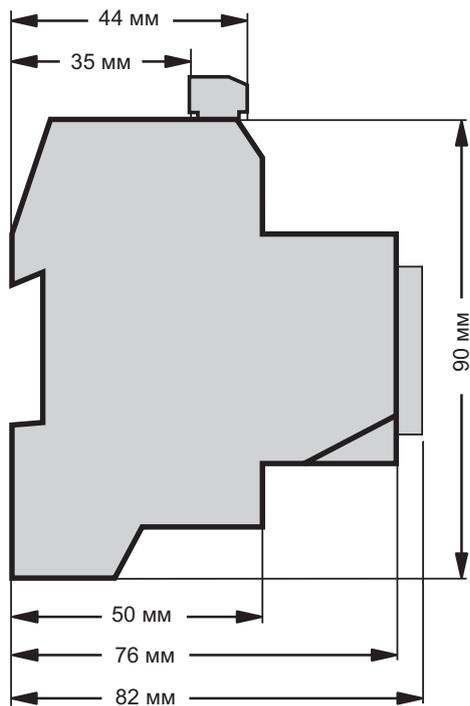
PRO с монтажными размерами, схематический вид сбоку
